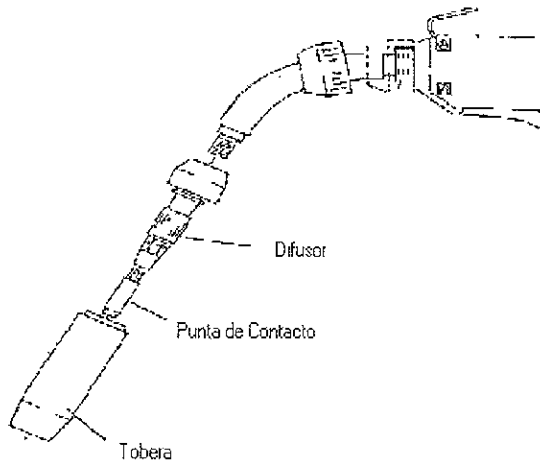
pistola soldadora para proceso GMAW y sus partes principales
